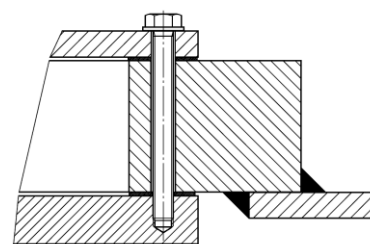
Arranjo de montagem com estrutura do coletor, tampa lisa e parafuso padrão.
